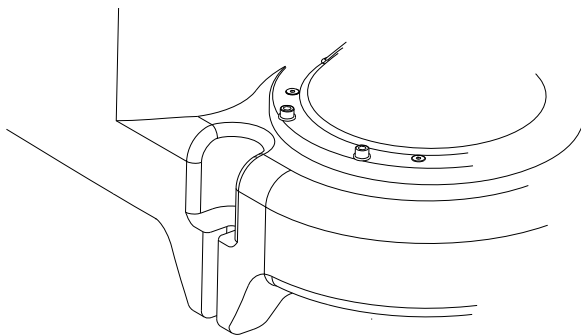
Точка крепления для монтажа резервуара на фундаменте
